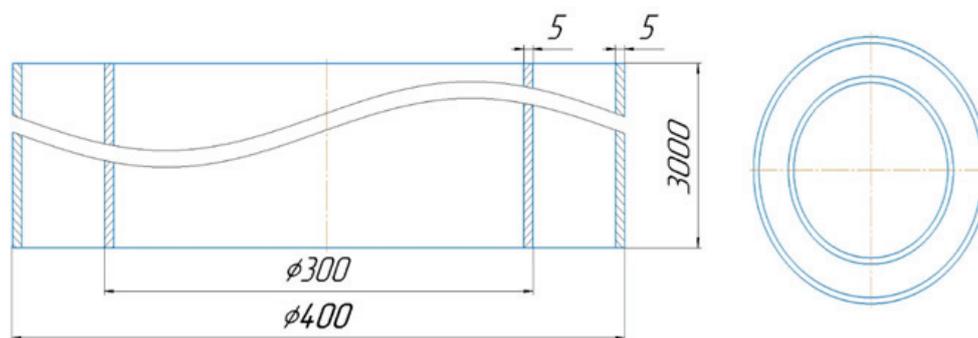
Эскиз двойной трубы: а) – вид спереди; б) – вид сверху
